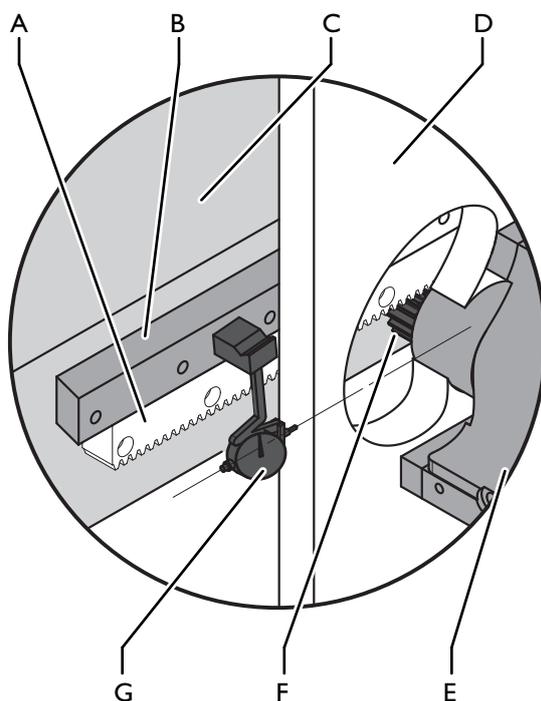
Проверить зазор в зацеплении: Стрелочный индикатор (точный метод)
